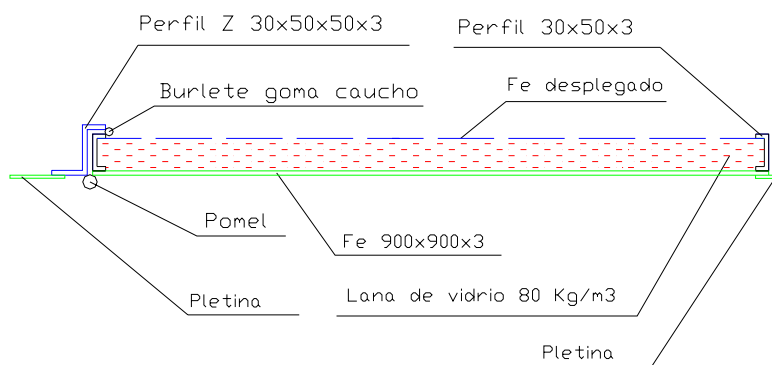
Diseño de puerta de acceso al motor. Vista superior para un paño. (Fuente: Elaboración propia).
